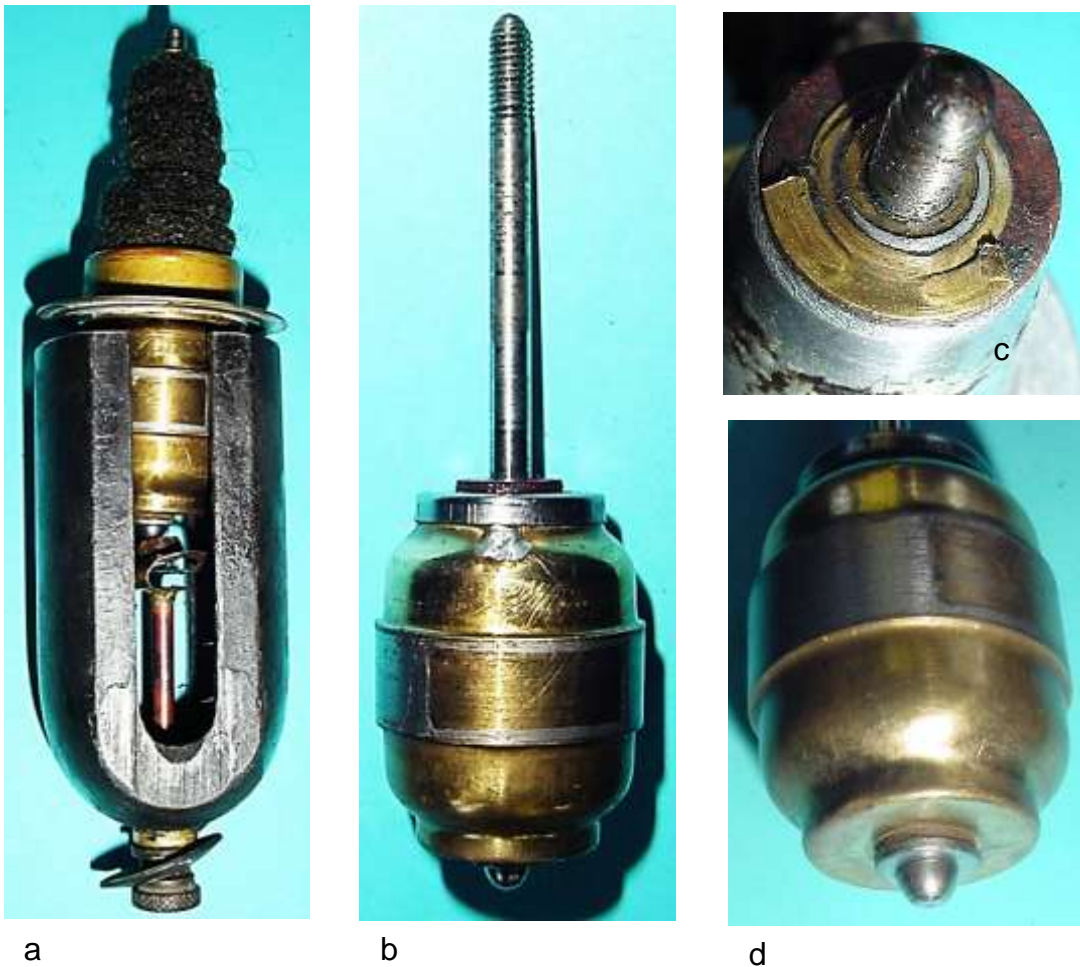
Anker: a) Position des Ankers im Polsystem, b) Anker mit Welle, c) Obere Anlaufscheibe, d) Anker mit Spannung führendem Knopf in der unteren Verschlusskappe
